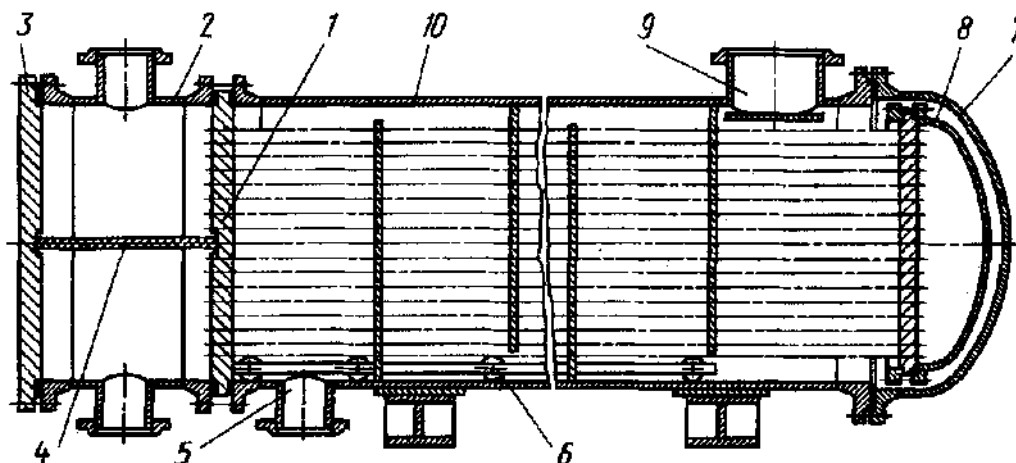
Горизонтальный двухходовой конденсатор с плавающей головкой
